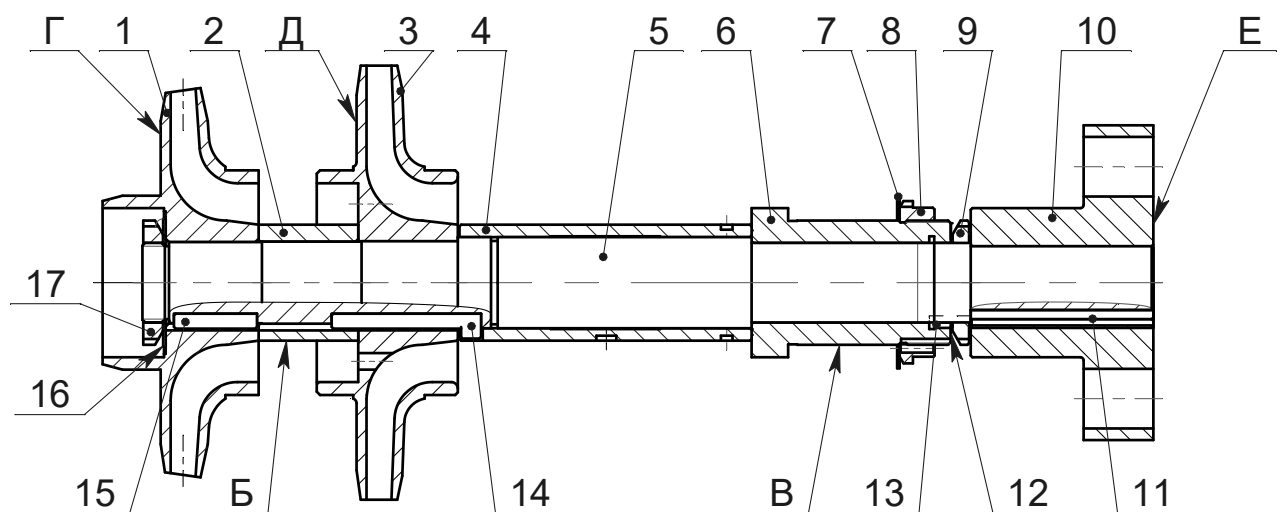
Вал быстроходной части в сборе для поставки в качестве ЗИП насосов 1КсВ125-140-..., 1КсВ100-100-..., 1КсВ200-130-..., 1КсВ200-220-..., 1КсВ315-160-...
